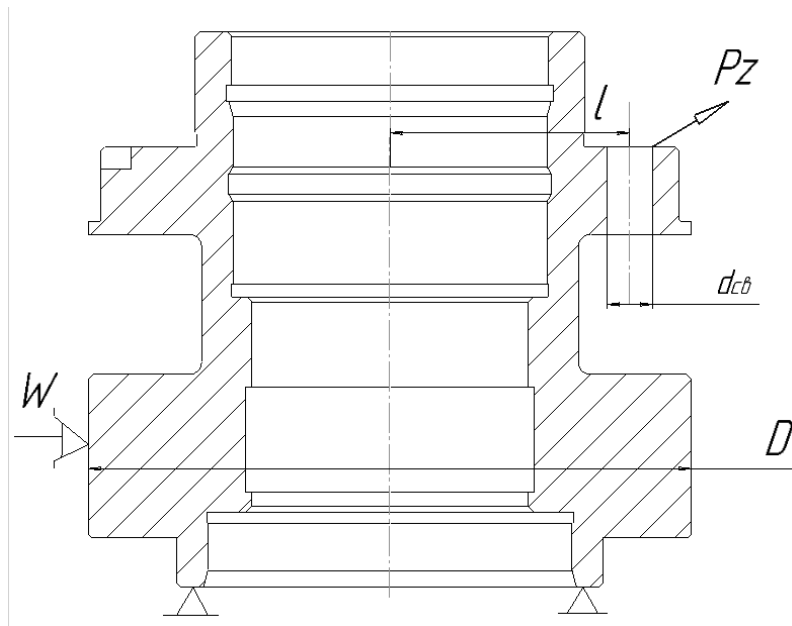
Схема базування та закріплення деталі корпус
